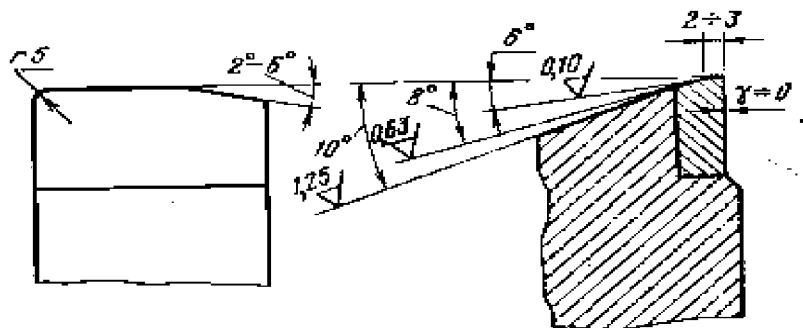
Стругальный резец для чистовой обработки плоскостей
